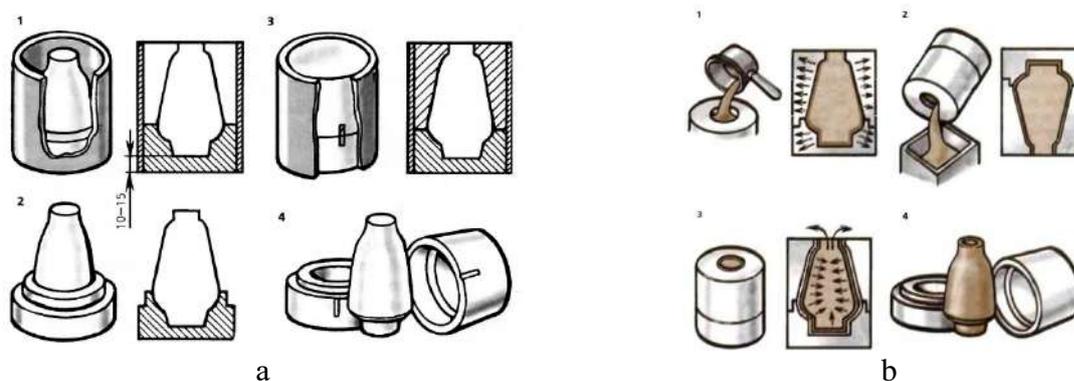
Этапы создания литейной формы и шликерного литья: а – процесс изготовления гипсовой формы для литья; б – процесс литья шликера и извлечения изделия из формы
